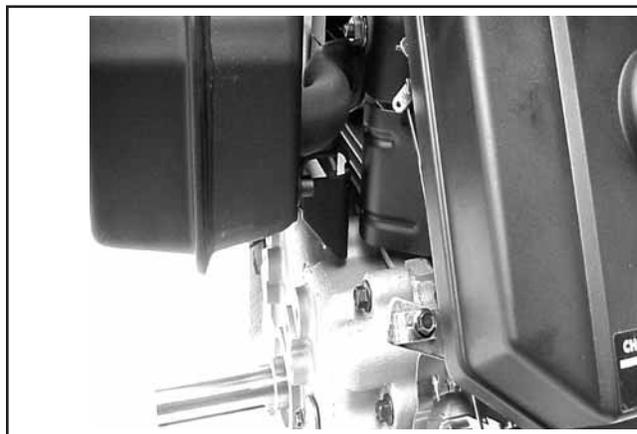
Borboleta Remota e Ajuste do Obturador de Ar.
